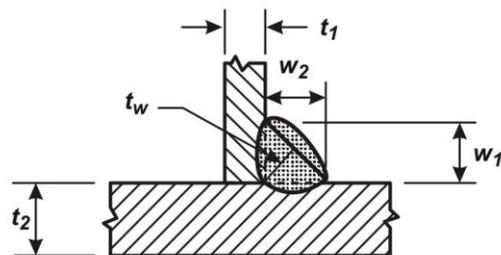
Uniones soldadas de solape o yuxtaposición con junta de filete.
